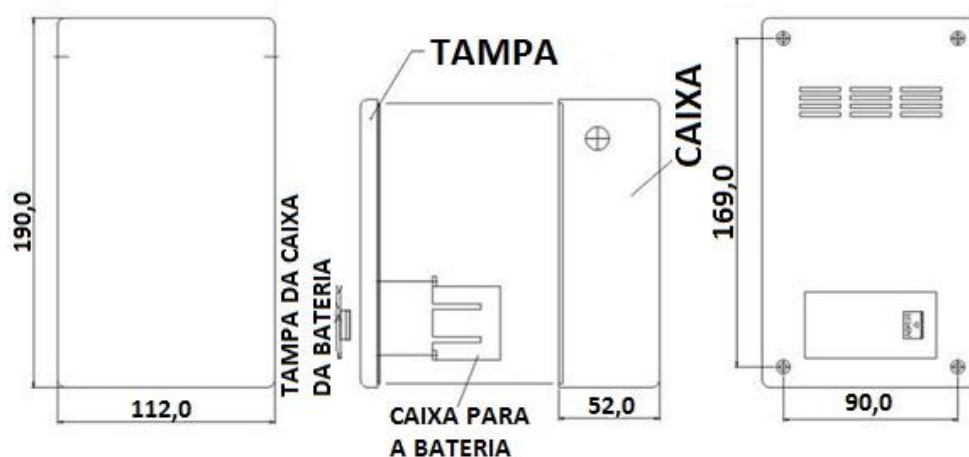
Caixa de plástico e dimensões em mm para acomodação do equipamento.
